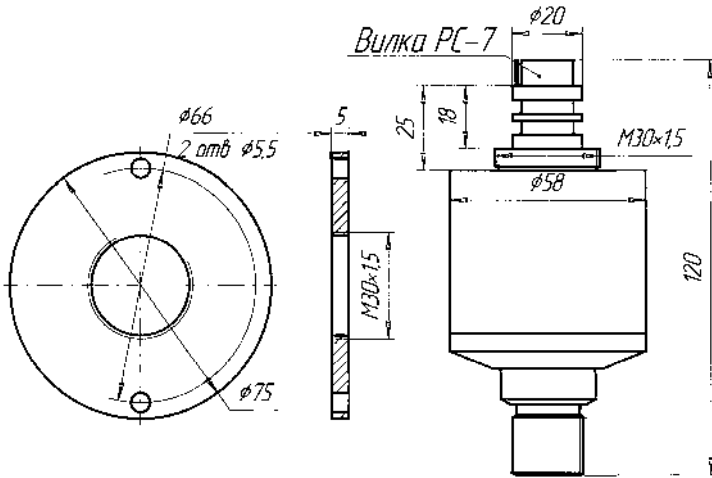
Модель 1220. Титановый корпус, гермопосадка.
